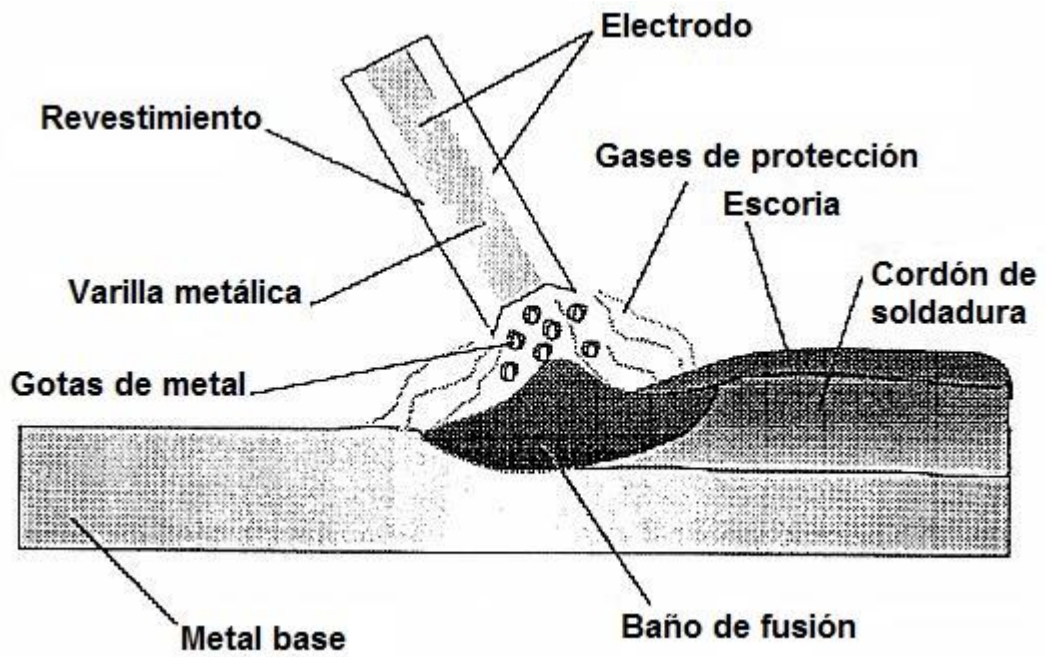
Esquema de soldadura pel mètode SMAW (Font: Ingemecanica)
